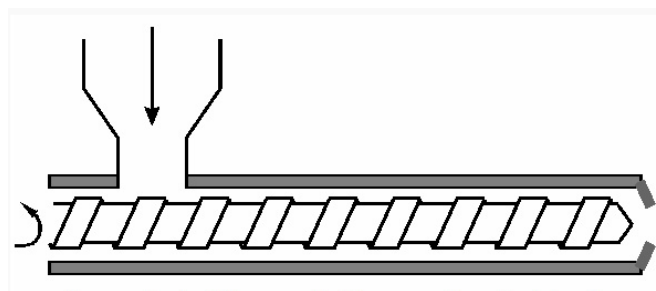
Cilindro o camisa que alberga el tornillo [21].
